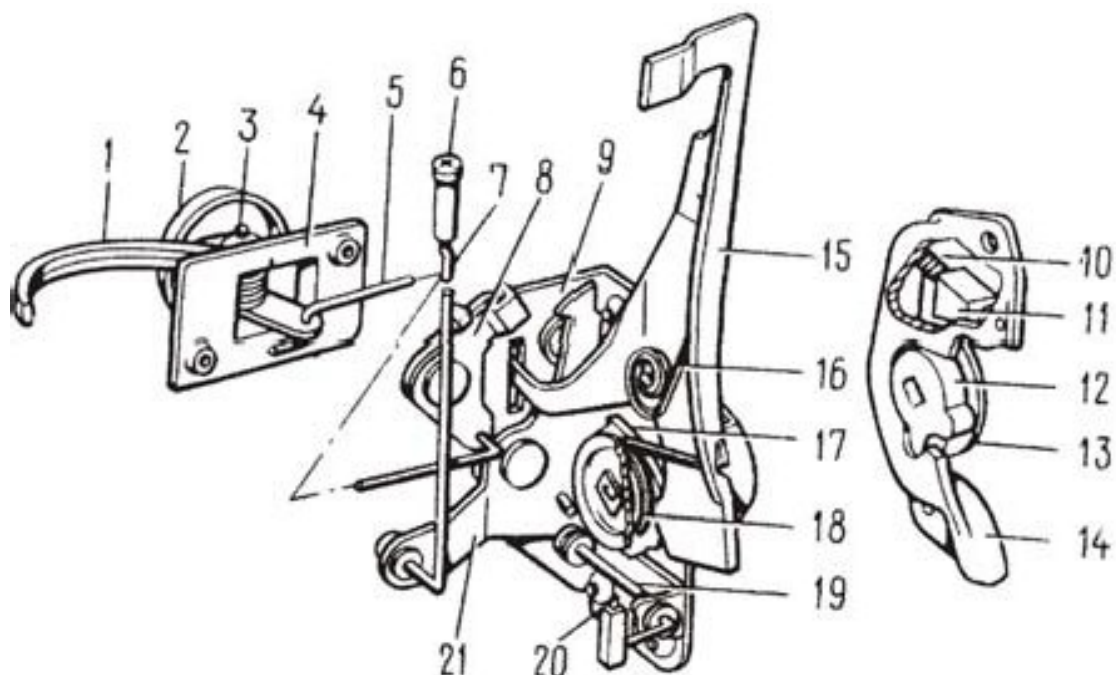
Замок передней левой двери: 1-внутренняя ручка двери; 2-облицовка внутренней ручки; 3-ось; 4-кронштейн внутренней ручки; 5-тяга внутренней ручки; 6-кнопка блокировки замка; 7-тяга кнопки блокировки; 8-рычаг внутреннего привода замка; 9-корпус замка; 10-пружина сухаря; 11-сухарь фиксатора замка; 12-ротатор; 13-опора центрального валика; 14-корпус фиксатора; 15-рычаг наружного привода; 16- пружина рычага наружного привода; 17-храповик; 18-пружина храповика; 19-валик выключения замка; 20-тяга выключения замка; 21-рычаг блокировки замка.
